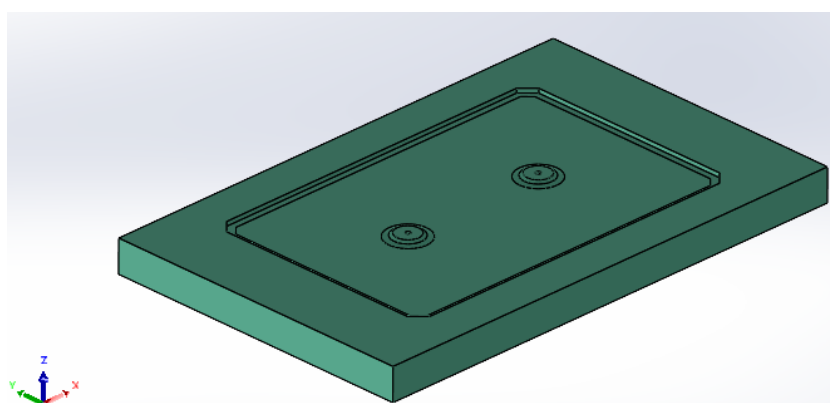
Representação isométrica do molde superior da placa de alumínio (*Solidworks*).
